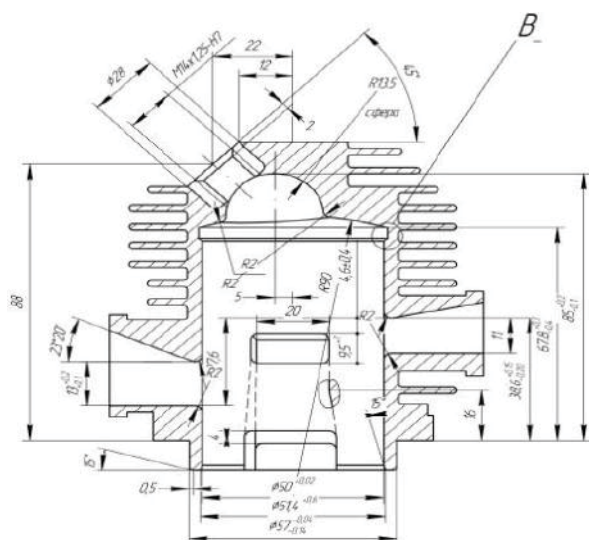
Корпусная деталь – цилиндр двухтактного двигателя
